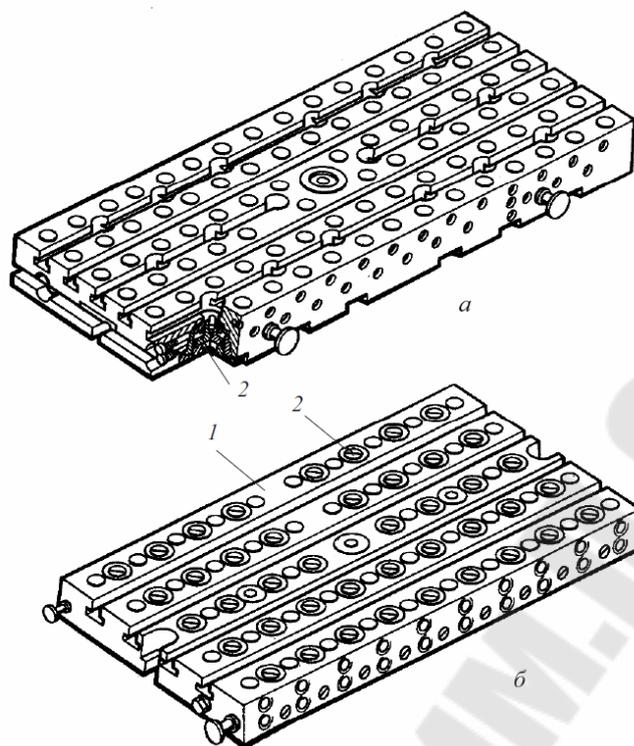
Прямоугольные гидравлические плиты сборно-разборного приспособления [4]
